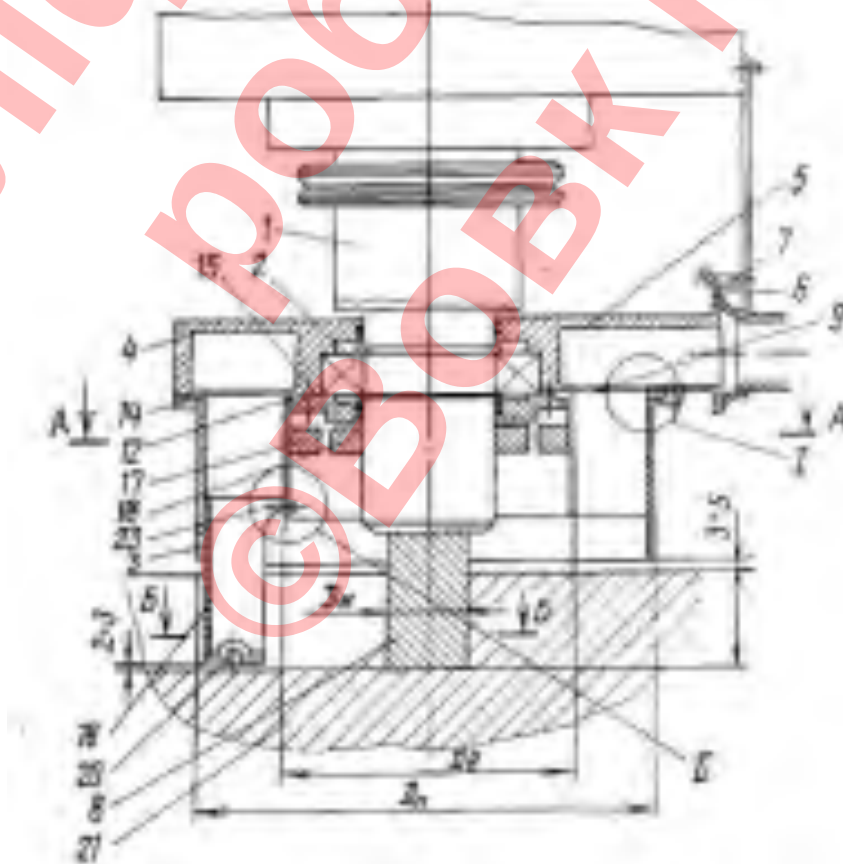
Схема пристрою видалення стружки 1291362
